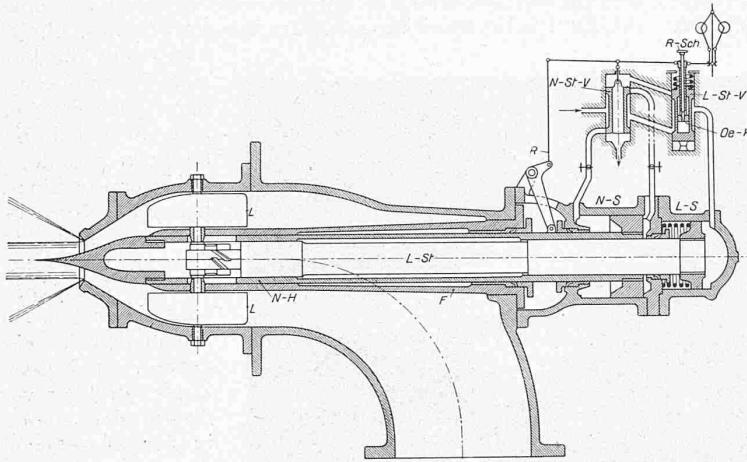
Universal-Regulierung System Seewer für Hochdruck-Pelton-Turbinen.
